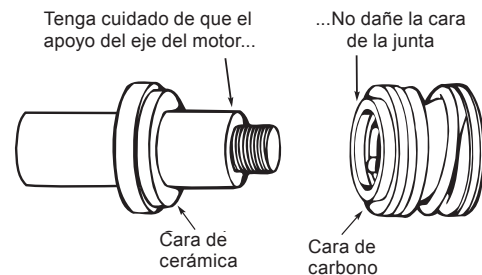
PROTEJA LAS CARAS DE LA JUNTA
